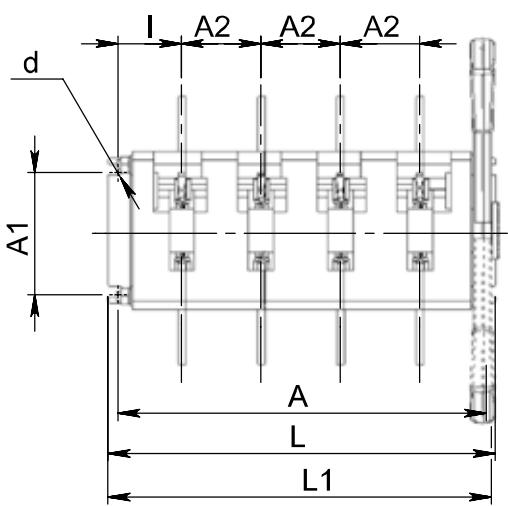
Выключатель-разъединитель на одно направление 4-полюсный с боковой смещенной рукояткой
